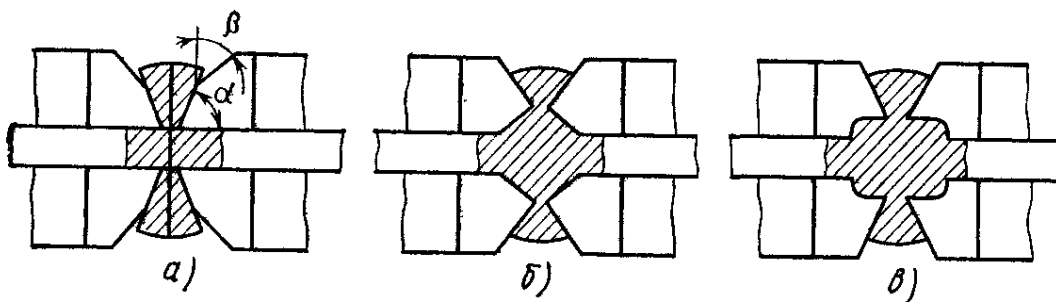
Схема сварки с принудительным формированием соединения
